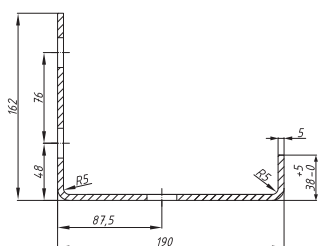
Placă de oţel utilizată pentru a prinde structura de fundaţie
